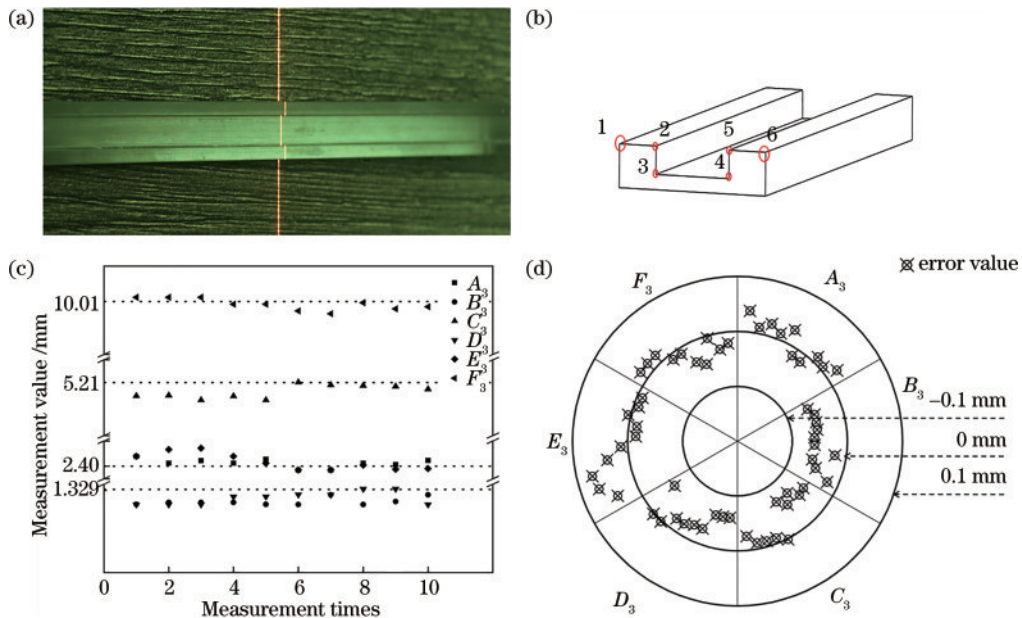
三号异型微小构件测量试验。(a) 构件原图; (b) 几何端点位置; (c) 构件各段尺寸测量; (d) 构件几何尺寸误差
